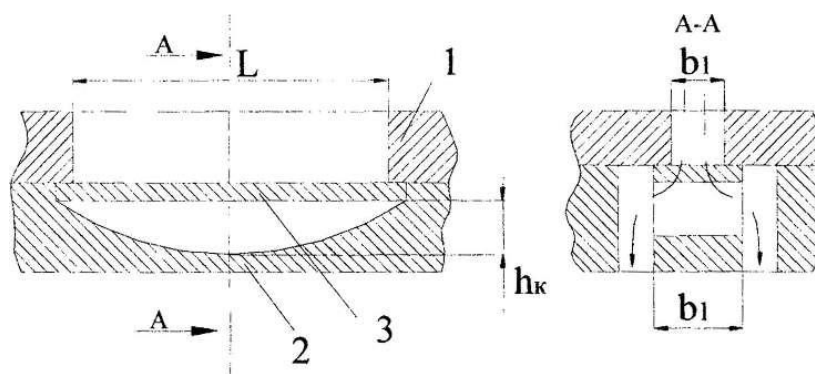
Пластинчатый полосовой клапан: 1 - седло; 2 - ограничитель подъема; 3 – пластина
